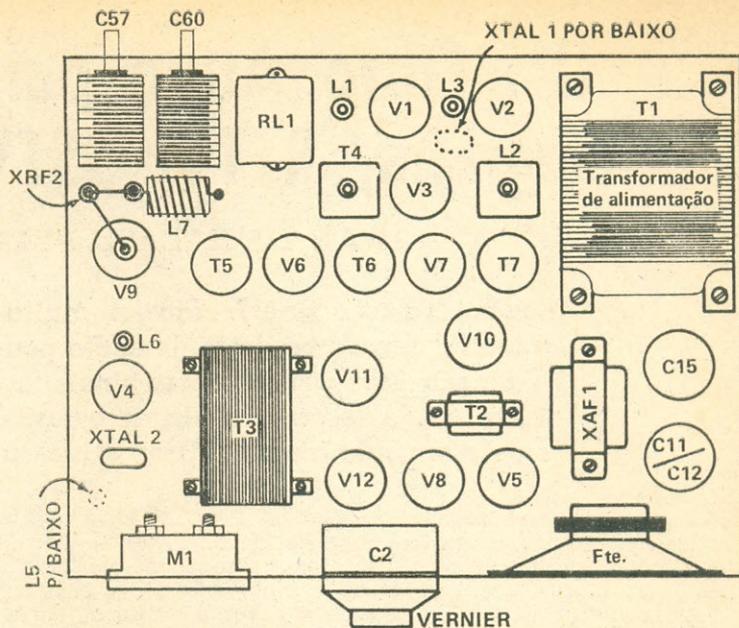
Disposição dos componentes sobre a face superior do chassi.
